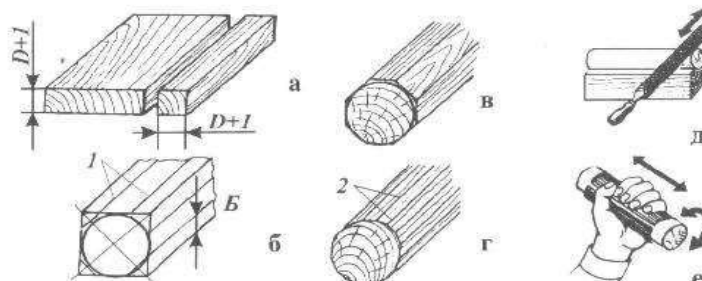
Последовательность изготовления детали цилиндрической формы ручным инструментом: а — выпиливание бруска квадратного сечения из доски; б — разметка торцов и граней заготовки; в — восьмигранная форма заготовки; г — шестнадцатигранная форма заготовки; д — обработка круглой формы напильником; е — зачистка шлифовальной шкуркой
